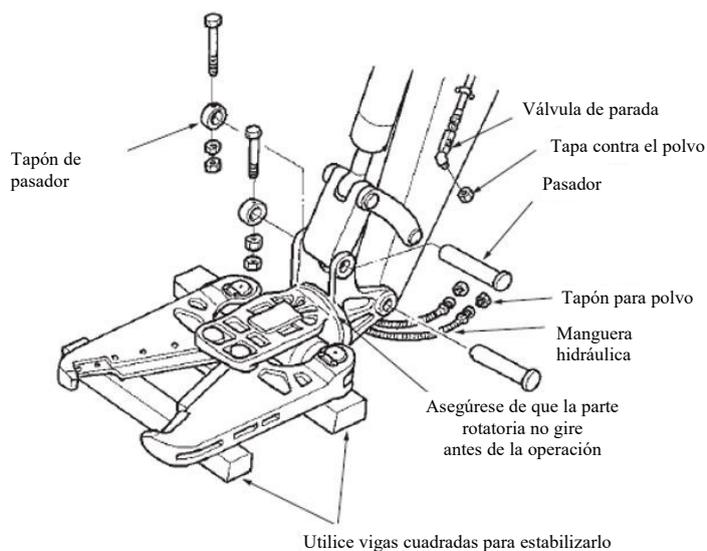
Ejemplo de desmontaje de una herramienta de corte de marco de acero
